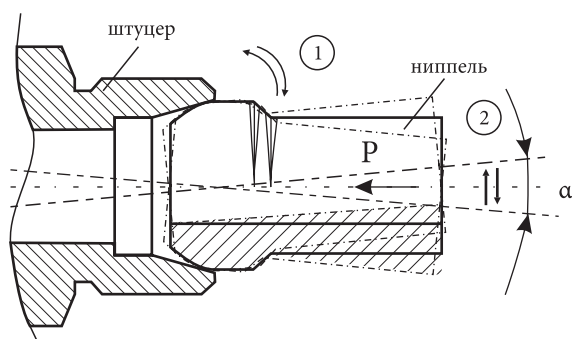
Схема создания герметизирующего соединения: 1 – возвратно-вращательное перемещение, 2 – угловое осциллирующее перемещение, Р – осевая нагрузка
